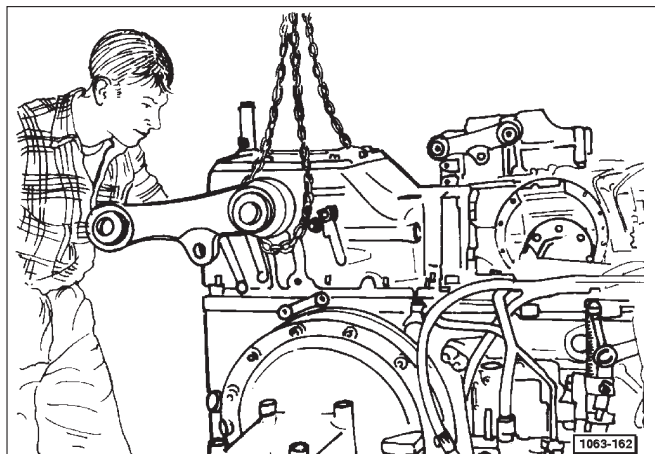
Poser le carter du relevage sur le carter de boîte de vitesses.
